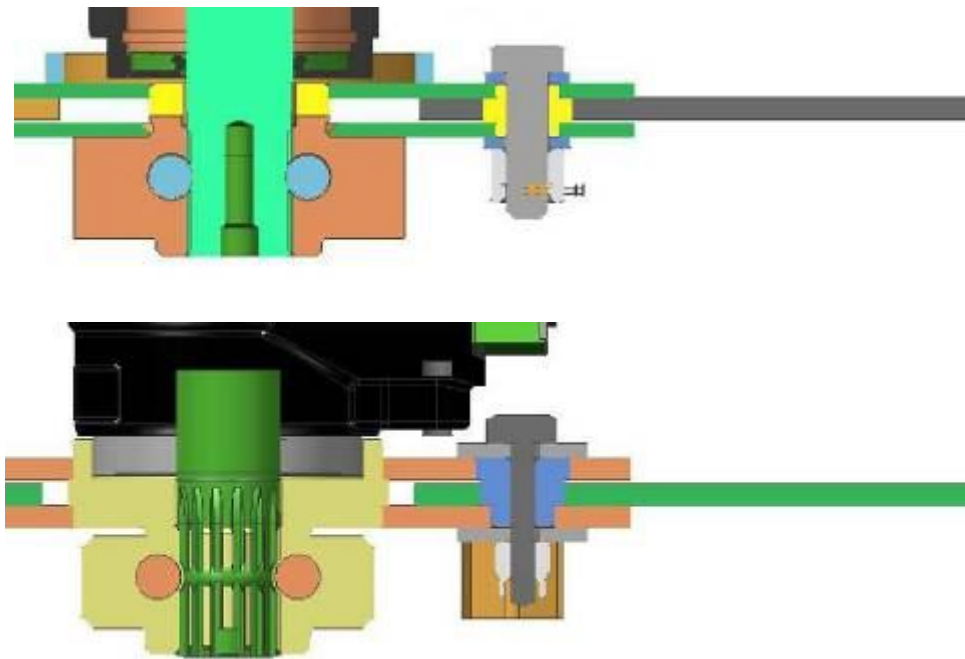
Измельчитель серийного приспособления (сверху)
